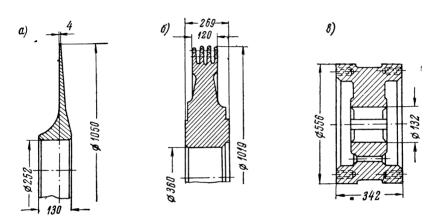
Қонструкции фланцевых валов: a — однофланцевый полужесткий; b—однофланцевый жесткий; e—однофланцевый вал-шестерня.
